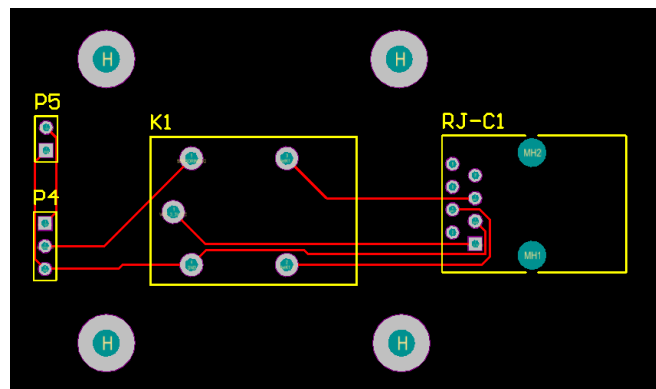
Diseño de PCB de módulo de RPM en Altium Design.
